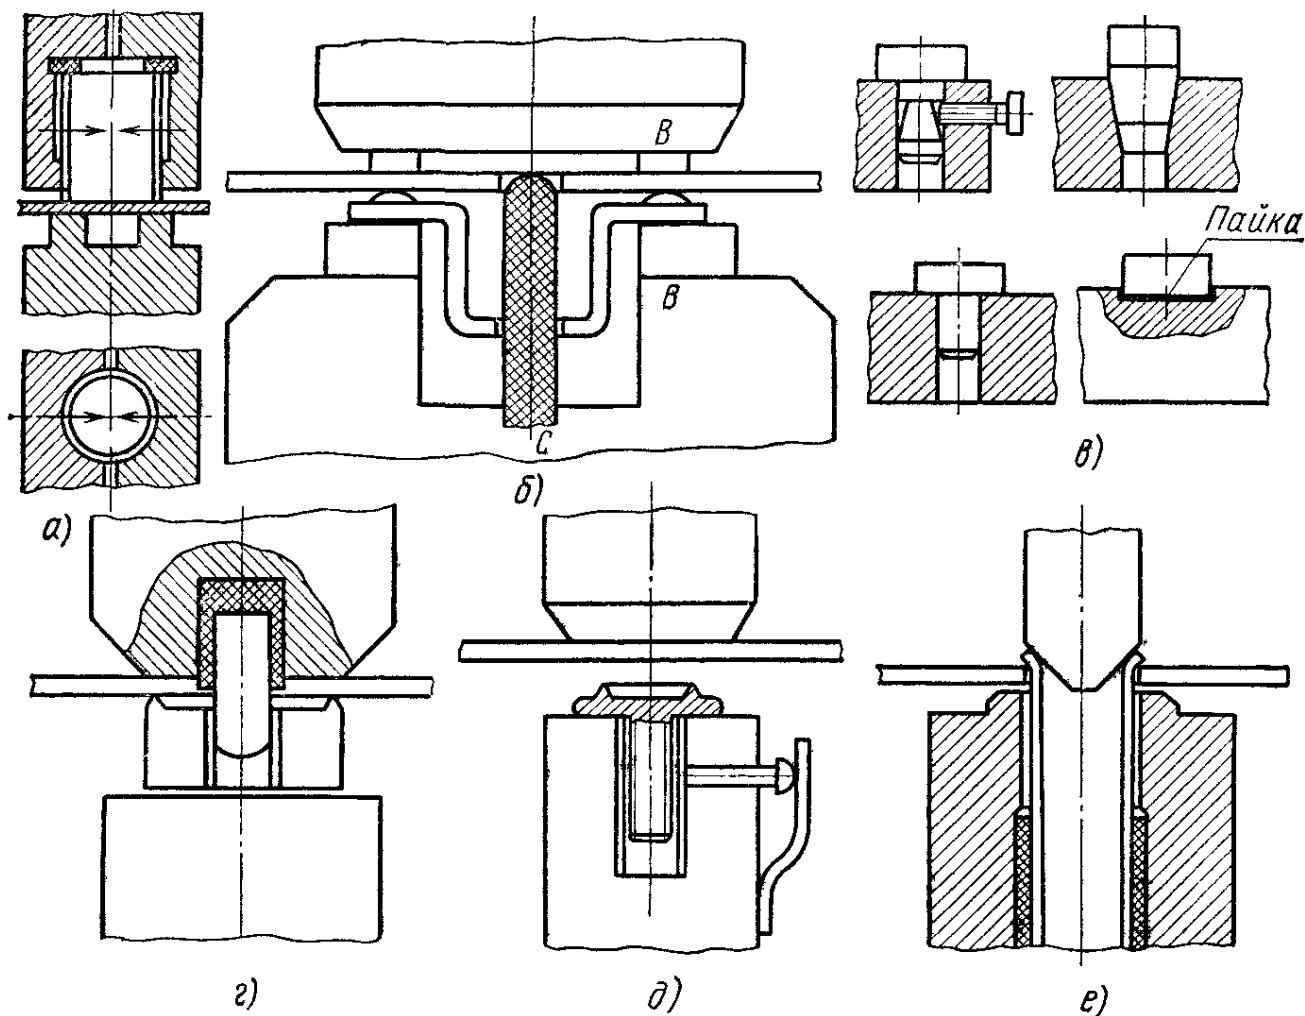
Приспособления для рельефной сварки (а, б, в, г, д, е) и схемы крепления электродных вставок (в)
